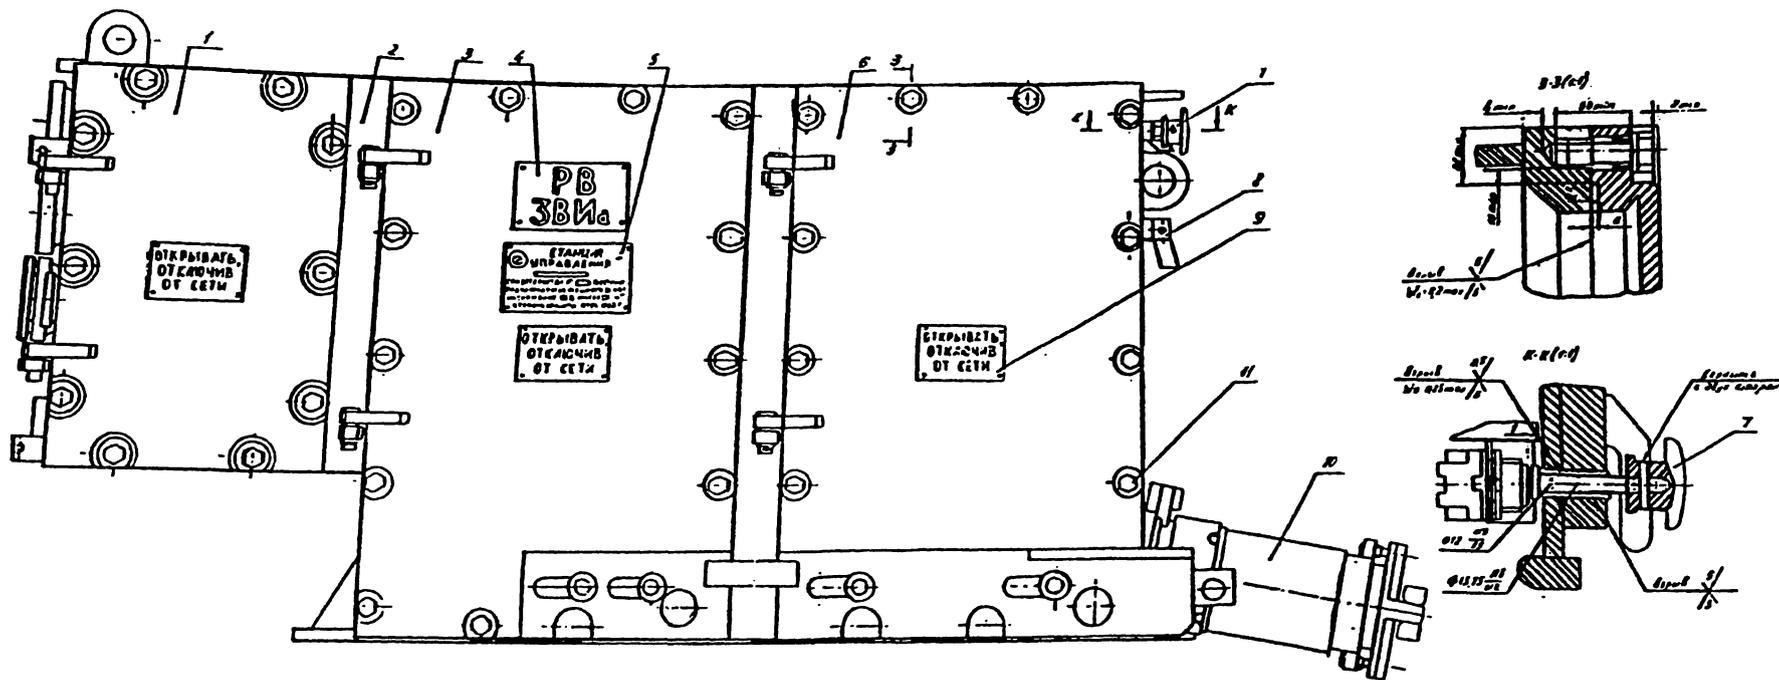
Общий вид станции управления комбайна «Урал-60»: 1 – крышка; 2 – корпус; 4,5,9 – таблички; 6 – крышка правая; 7 – ручка пускателя; 8 – ручка переключателя режимов работы; 10 – соединитель СНВ-260М; 11 – болт невыпадающий М16
